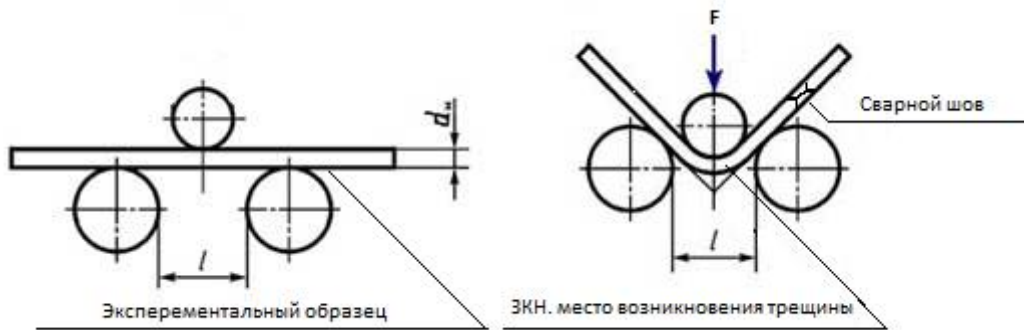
Схема испытания образца на сосредоточенный изгиб
